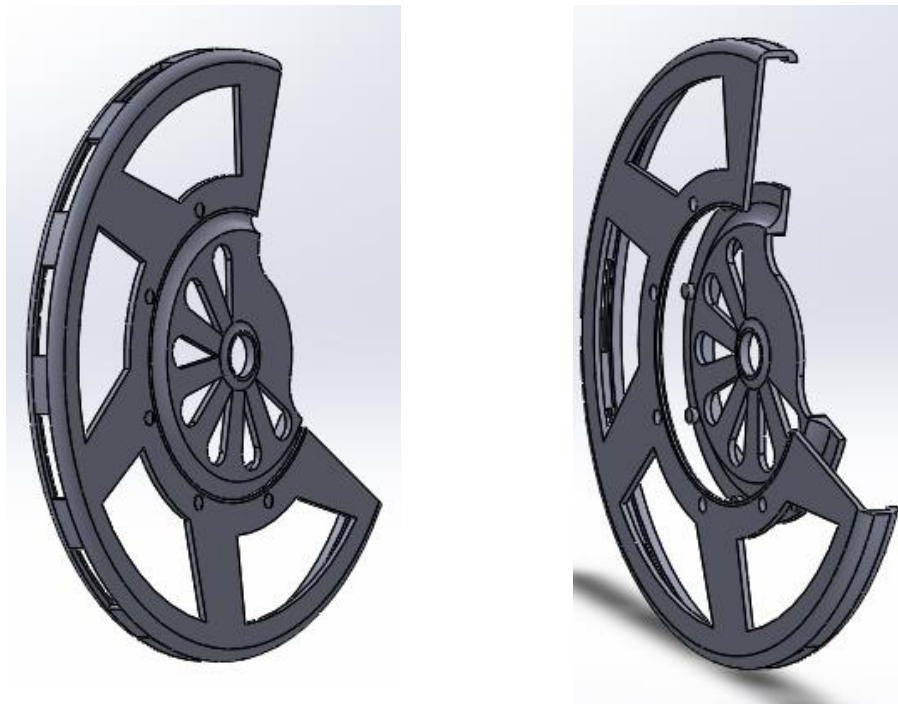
Vista del ensamblaje del modelo final de la protección delantera.
